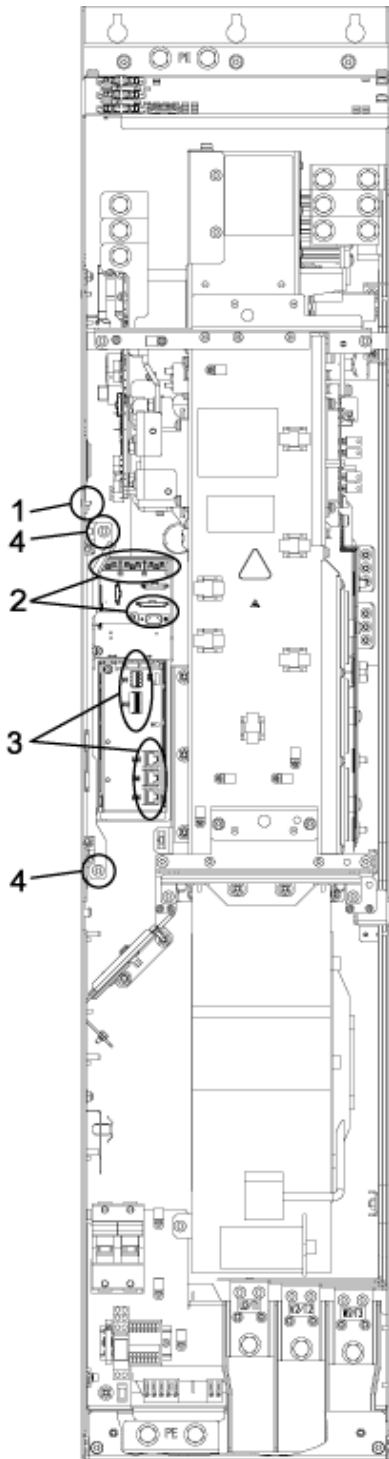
Austausch Control Interface Board, Baugröße GX
